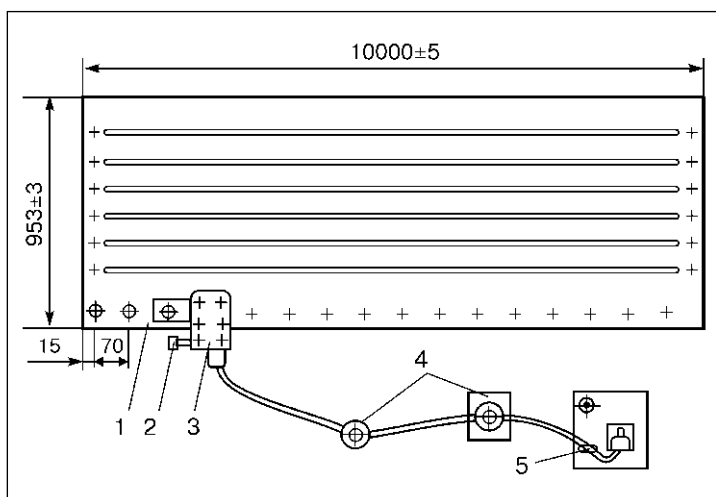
Базирование головки-пресса при пробивке отверстий: 1 — установка; 2 — рукоятка; 3 — головка-пресс; 4 — консоль шарнирного типа; 5 — гидрораспределитель
